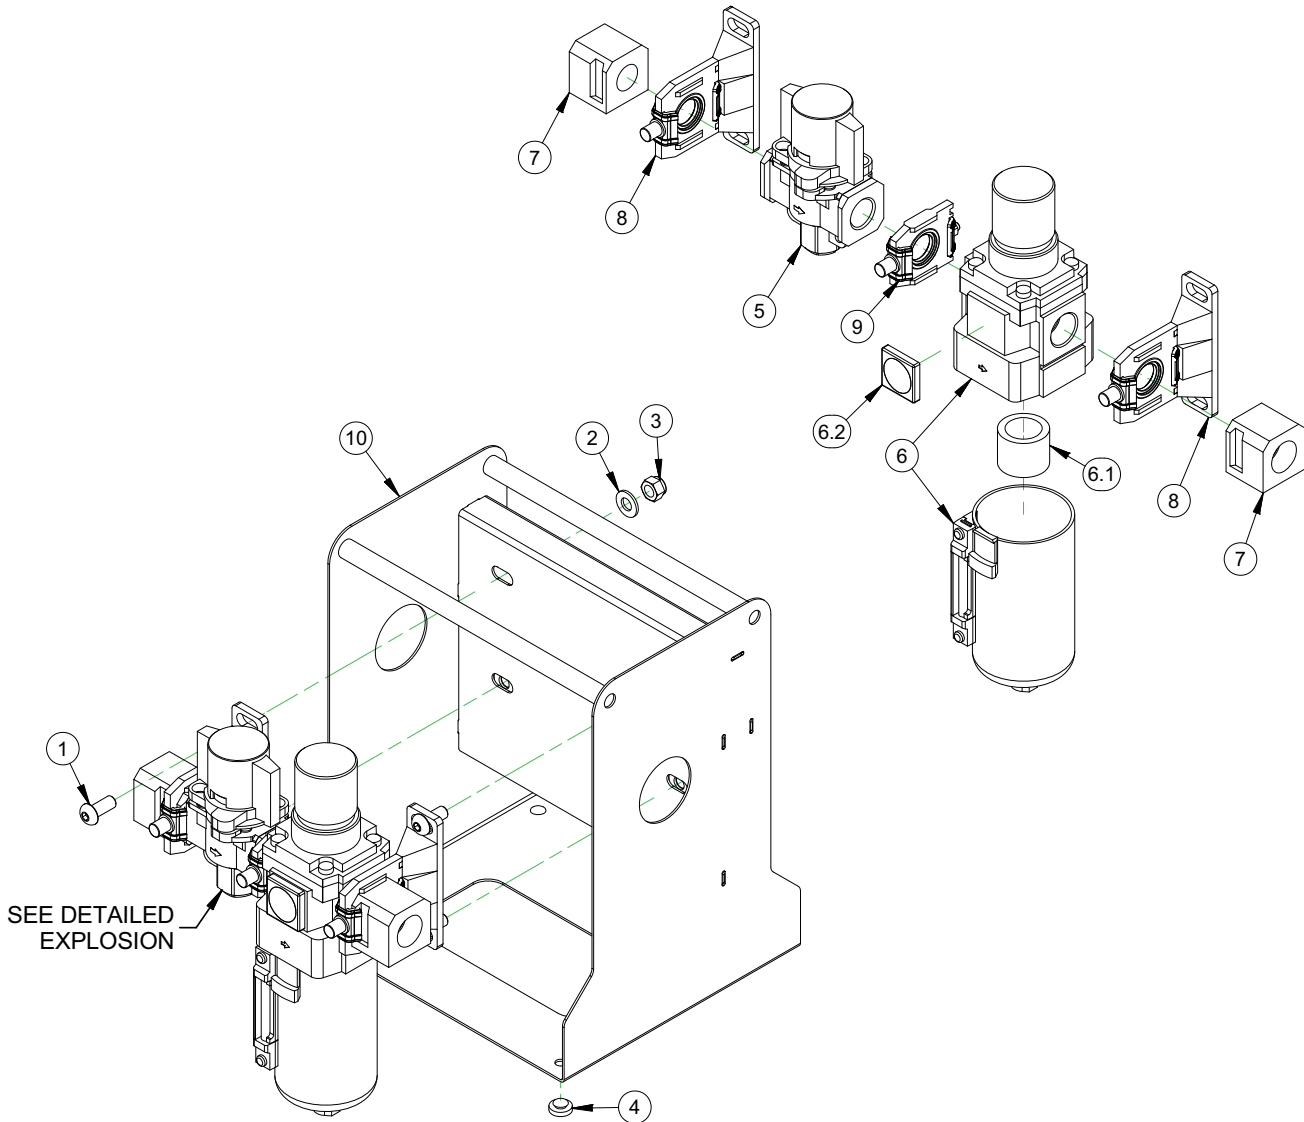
Список деталей для одноточечной сборки (P/N 62037)
